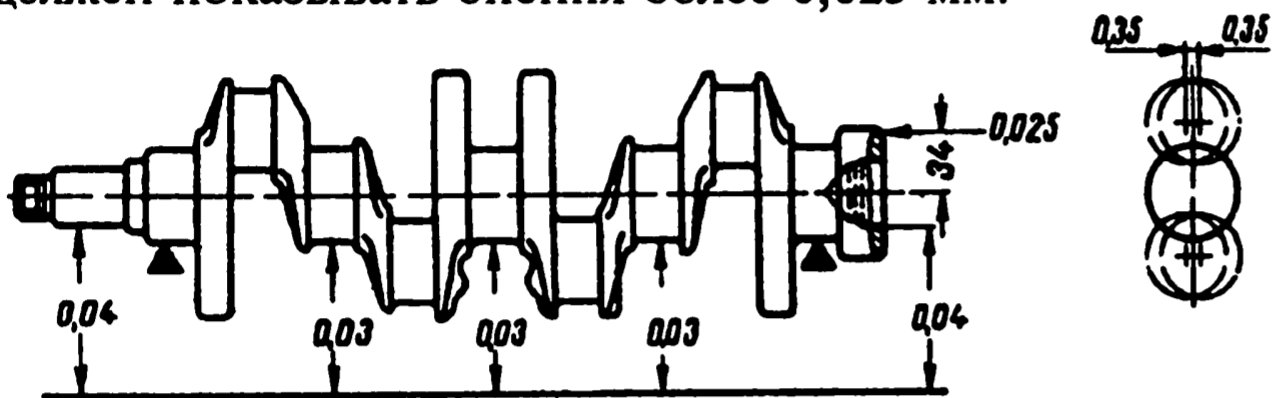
Допустимые биения основных поверхностей коленчатого вала
